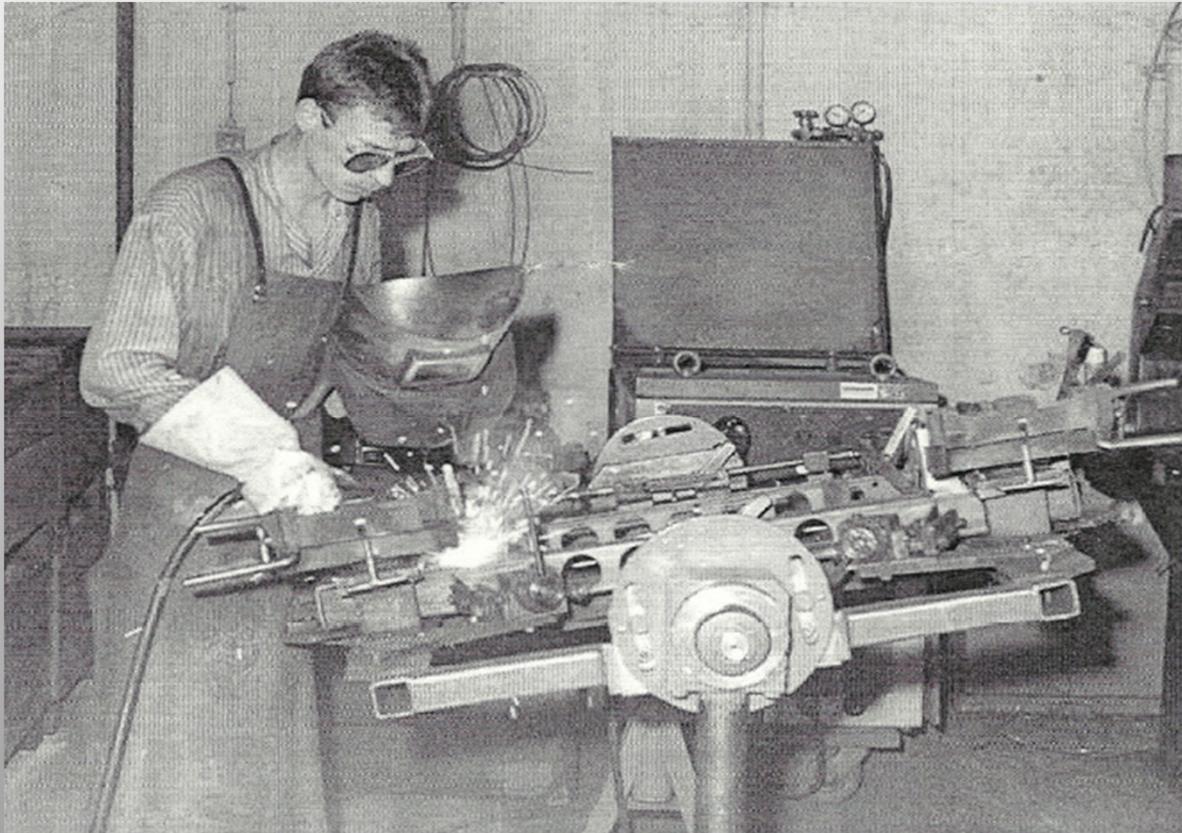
Handschweißarbeitsplatz mit Drehvorrichtung
